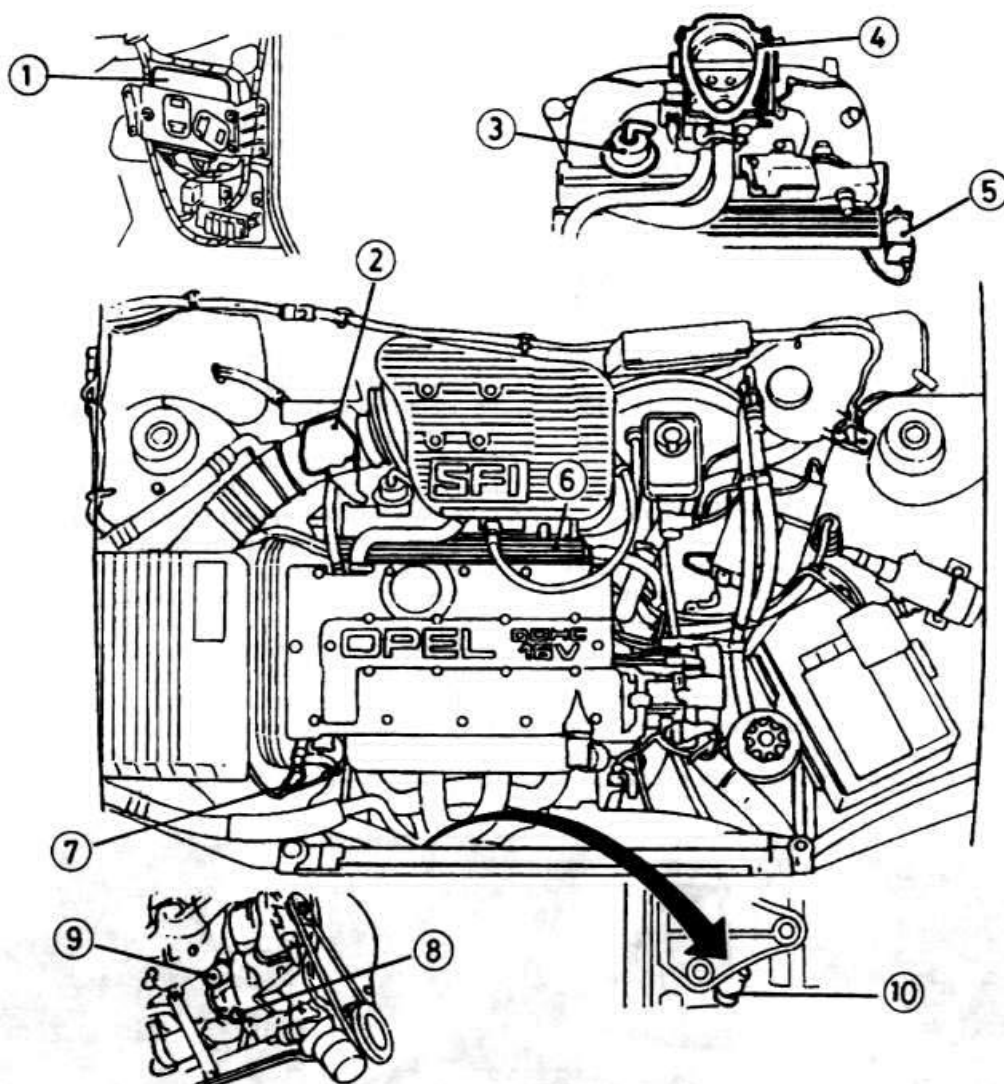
Система Motronic M2.5 впрыска топлива — двигатель с двумя распредвалами
